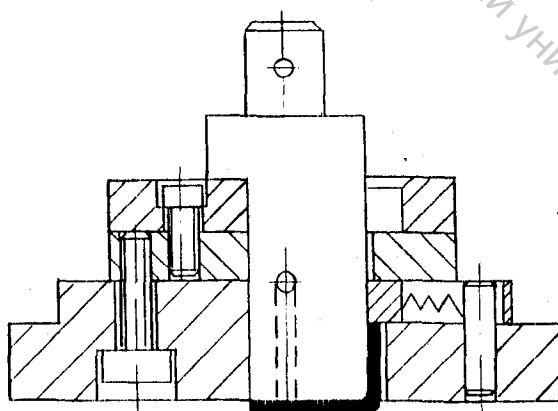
Пакет штампа для второй и последующих операций вытяжки коробчатых деталей без прижима.
